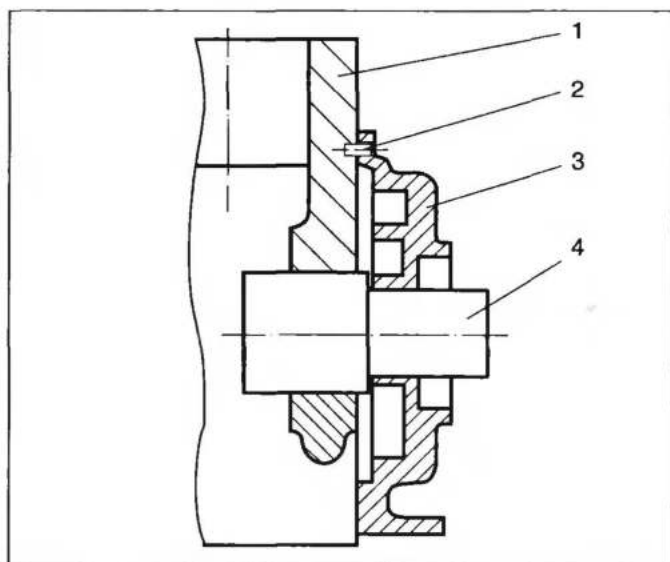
Перецентрировка корпуса масляного насоса после растачивания постелей коренных подшипников с помощью оправки:
